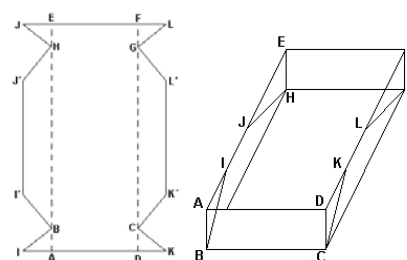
Elementul de bază pentru forma paralelipipică [5]
